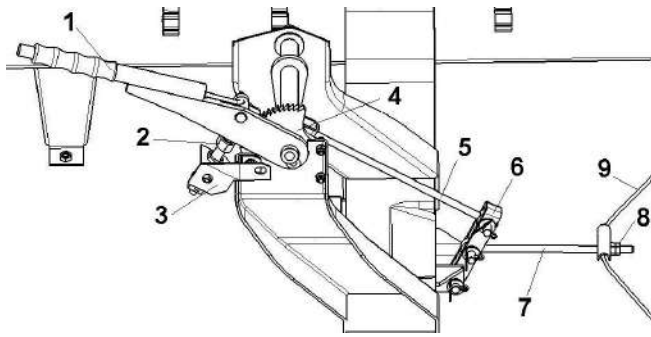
Привод стояночного тормоза: 1- рычаг включения стояночной системы; 2- включатель контрольной лампы; 3- кронштейн крепления включателя контрольной лампы; 4- кронштейн рычага в сборе с зубчатым сектором; 5- передняя тяга; 6- рычаг привода; 7- задняя тяга; 8- регулировочная гайка с контрагайкой; 9- трос стояночной системы
